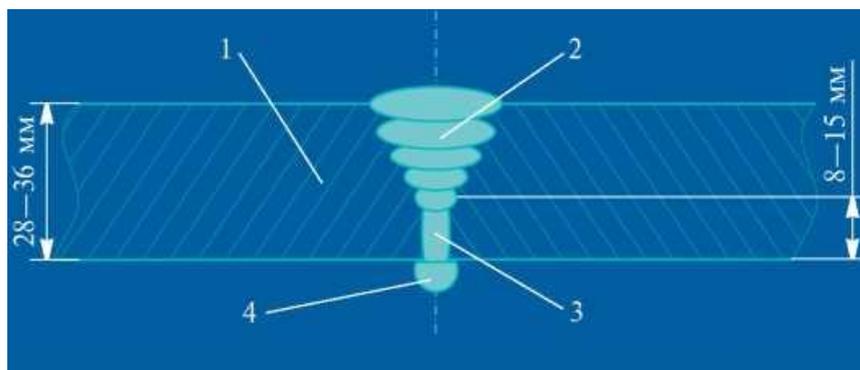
Схема сварного соединения, выполненного по технологии комбинированной сварки: 1 — стенка трубы; 2,3 — дуговая и контактная сварка соответственно; 4 — внутренний грат [5]
